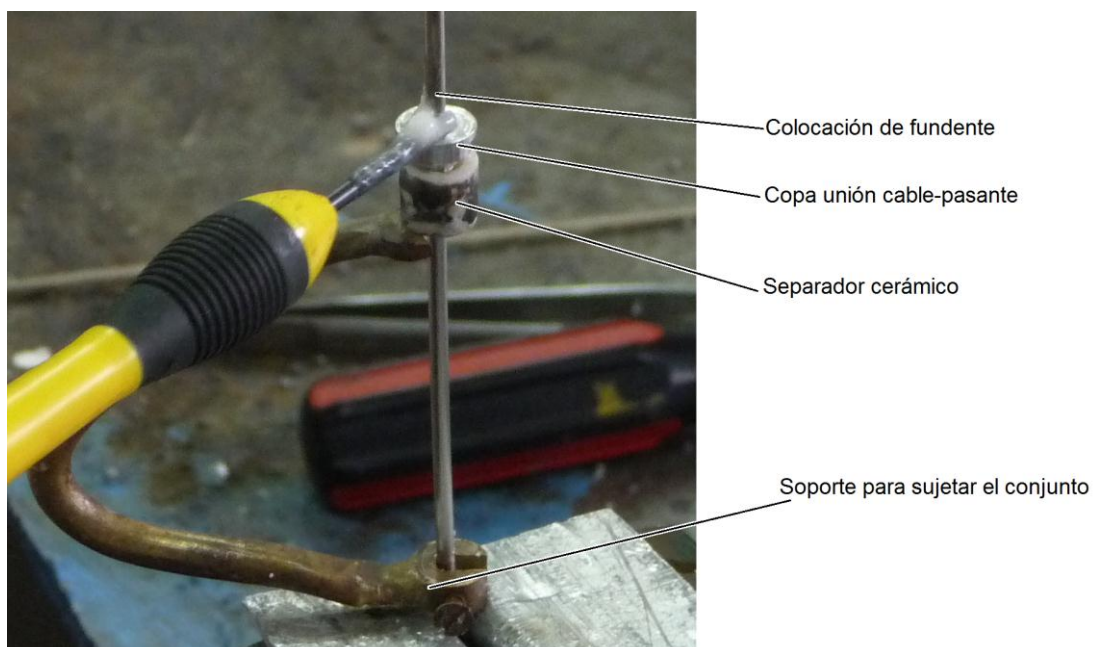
Colocación del fundente (o decapante) en la zona a soldar del cable y la pieza, el cual proteger de la oxidación durante la soldadura.
